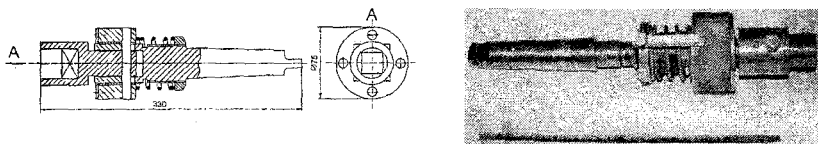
Изготовленный в ЮУрГУ патрон резьбонарезной для получения резьбы Tr33,5x3 - 6H
